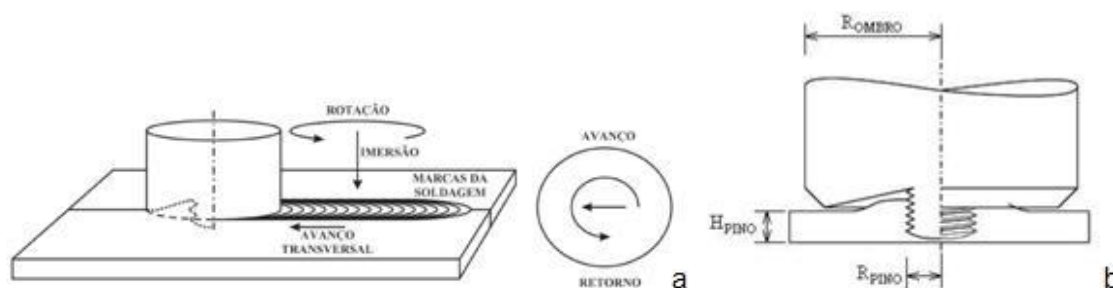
a) Esquemática do processo de soldagem por fricção linear. b) Vista lateral da ferramenta de soldagem por fricção linear (Fonte: Centeno, 2008).
